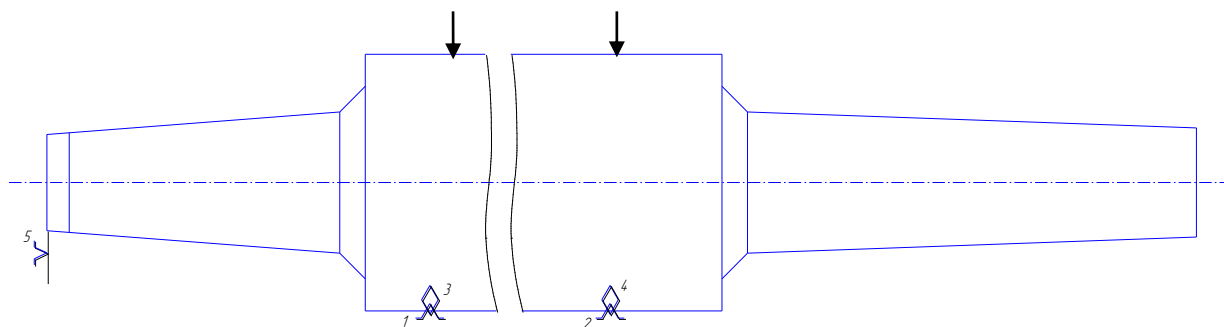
Теоретична схема базування валка на горизонтально-розточній і фрезерній операціях
